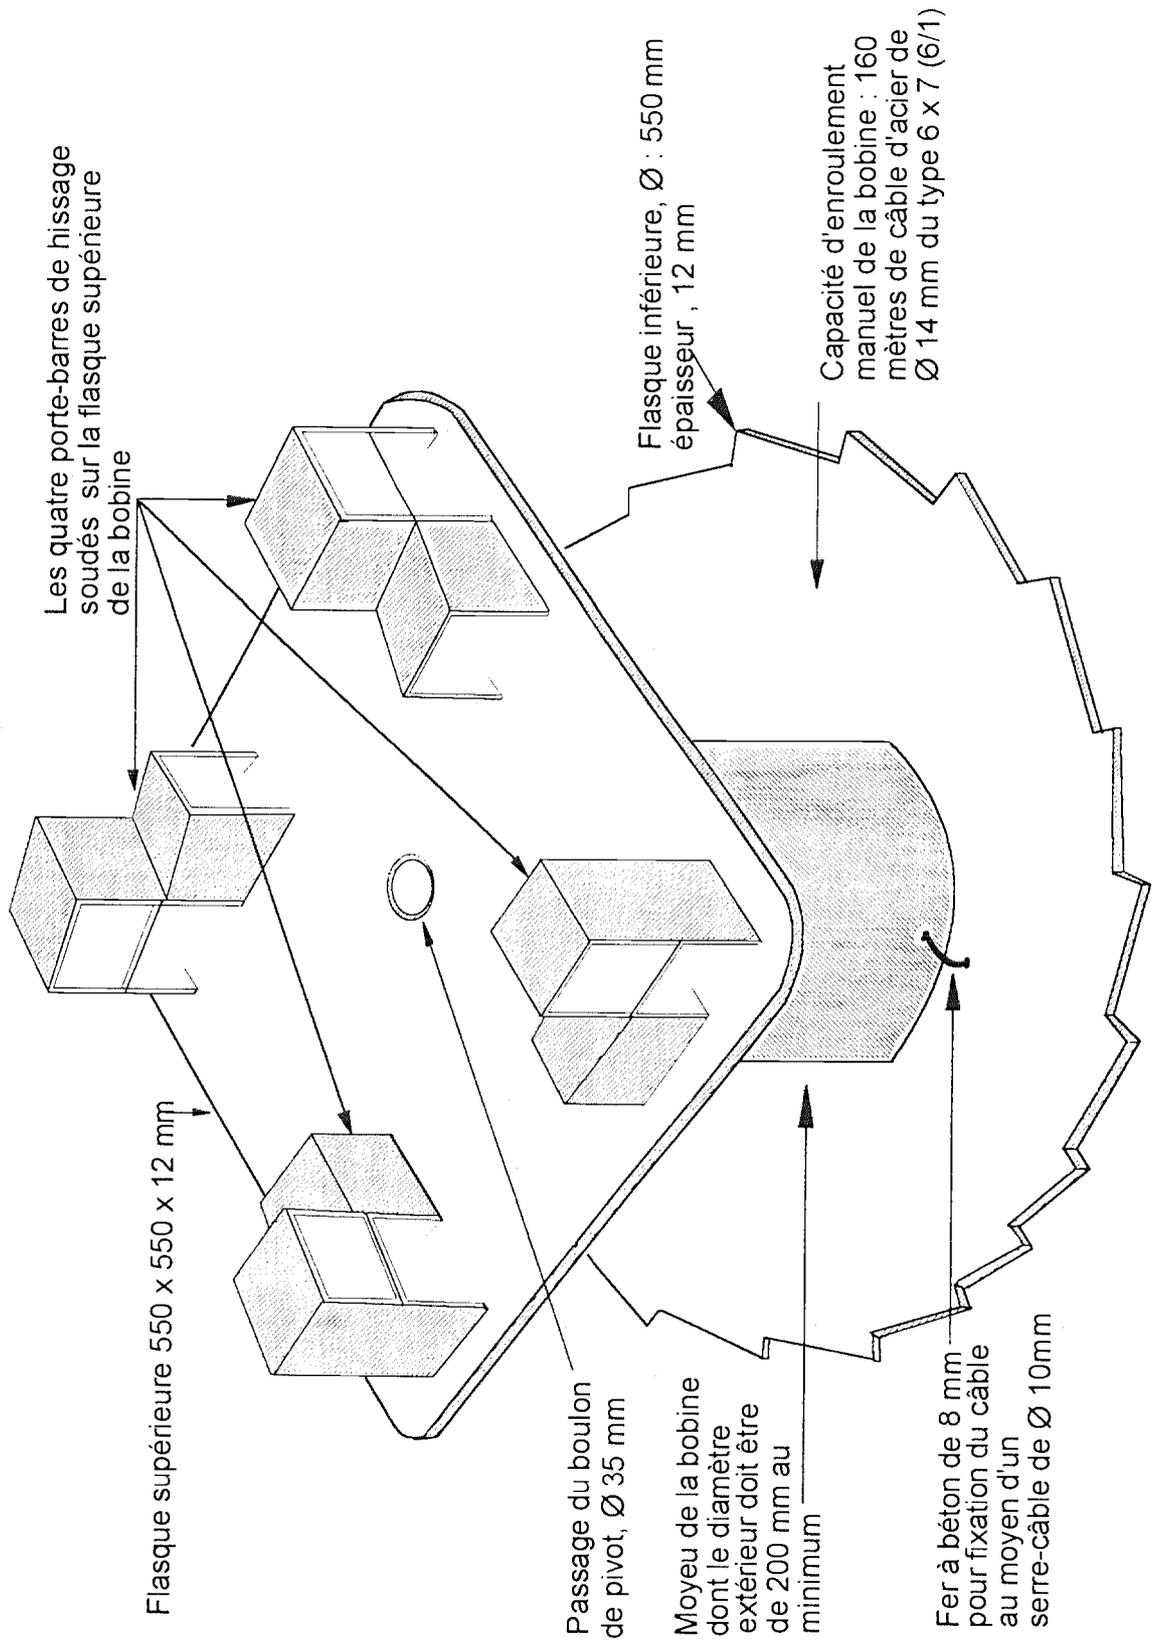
LA BOBINE DU CABESTAN COMPLETEMENT ASSEMBLEE
